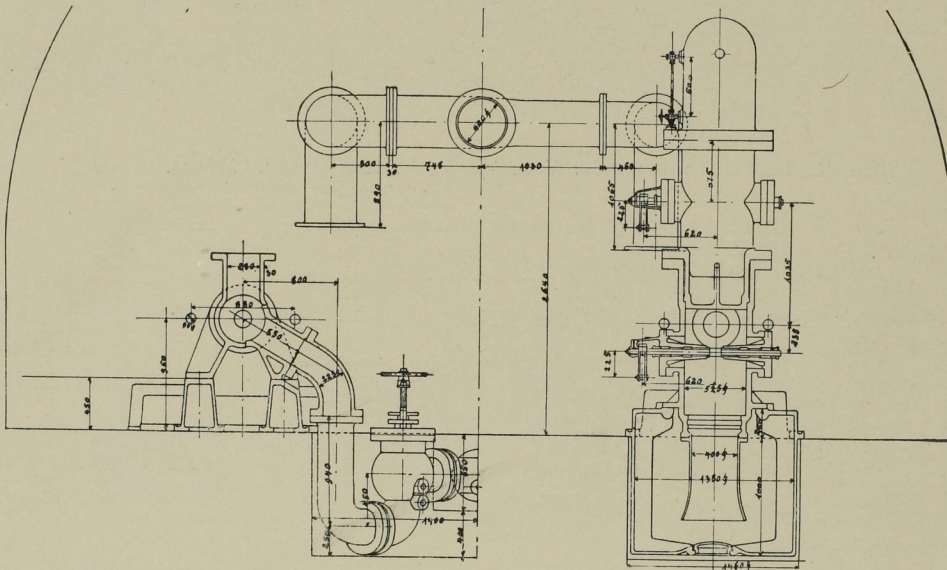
Querschnitt durch den Maschinenraum und die Druckpumpe. Masst. 1:60.
